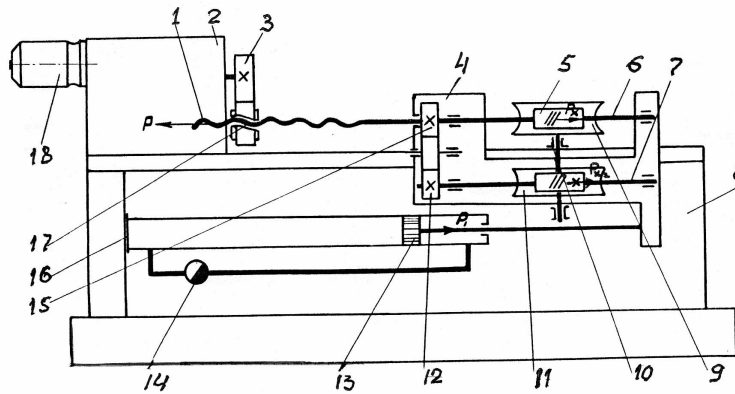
Схема механізму подачі зубофрезерного верстата
